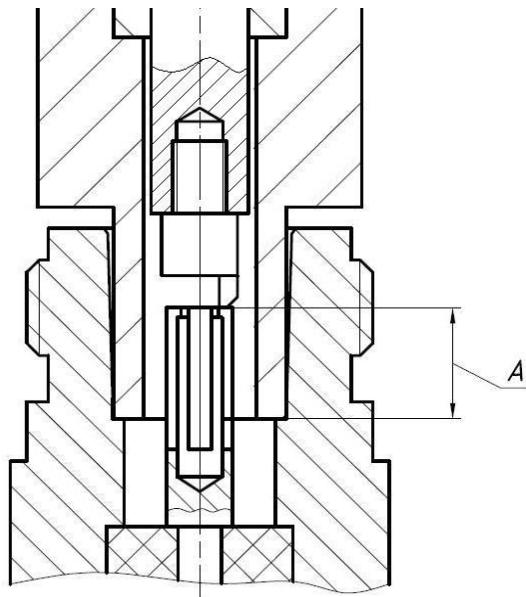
Проверка размера «А» соединителя «розетка»
